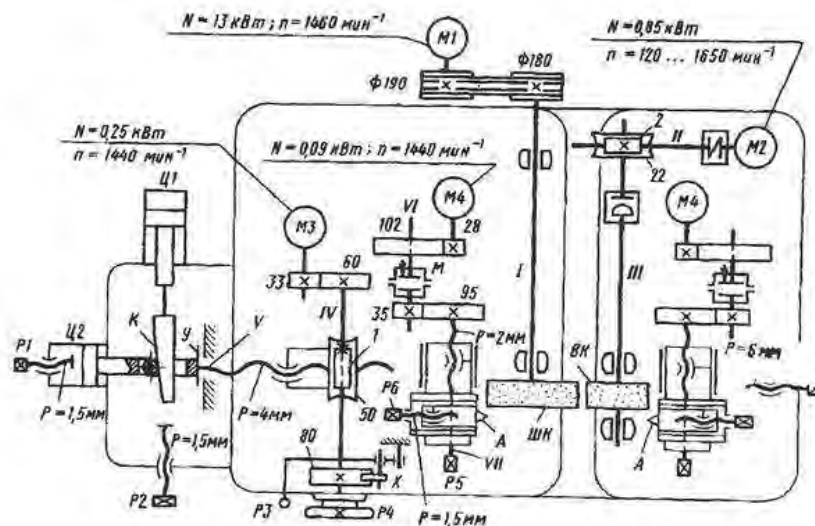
Кинематическая схема бесцентрово-шлифовального станка 3М184
